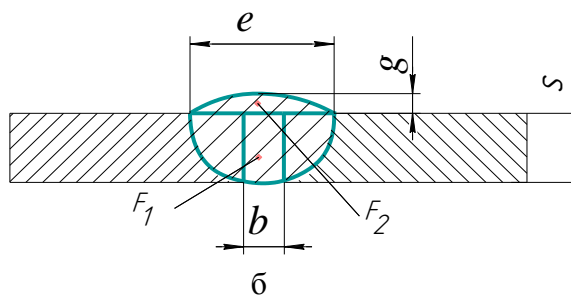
Форма поперечного сечения сварного соединения С2 после сварки:
